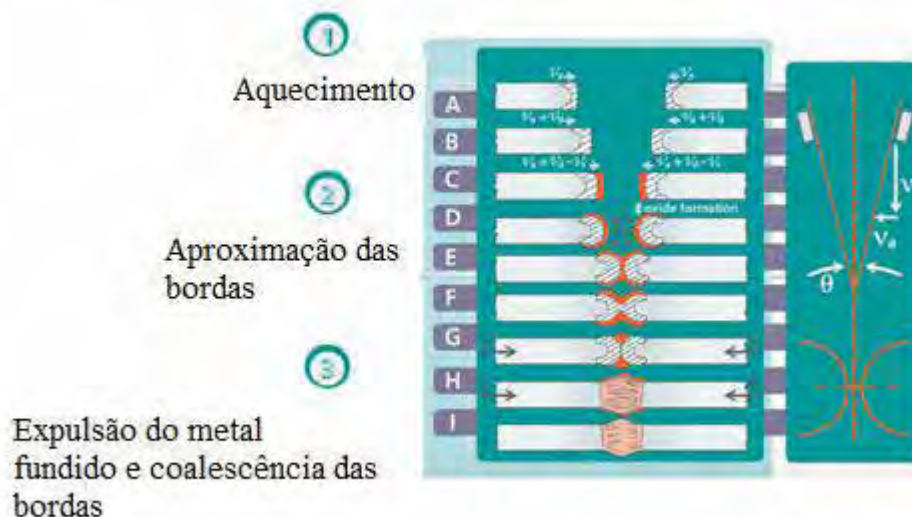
Processo de soldagem ERW (CUEVAS, A.; 2009)
